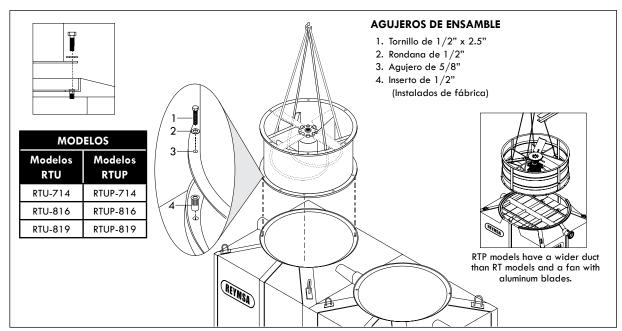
Instalación del ducto en una torre de dos ventiladores (RTU)
